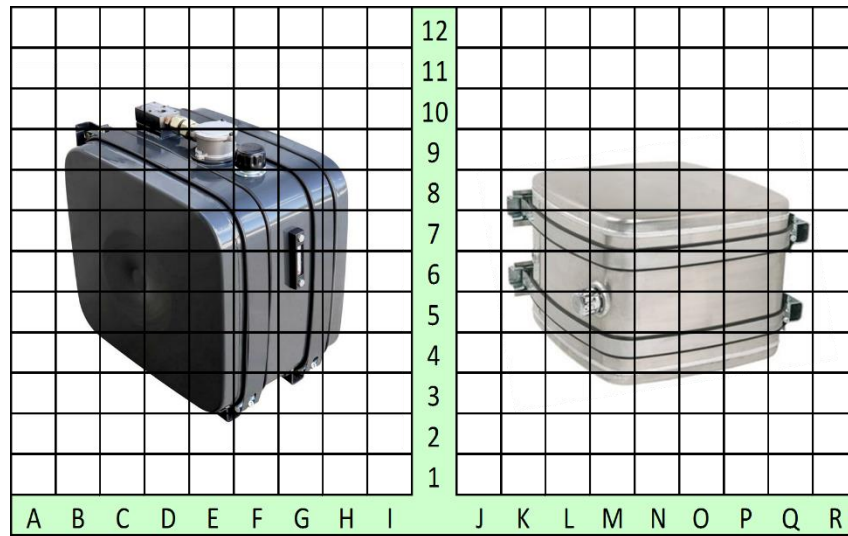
Ejemplo de mapa de localización para prueba de fugas y soldadura (30)
